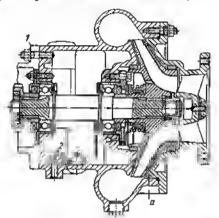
Vista general de una bomba con volutas de dimensiones disminuldas (dibujo de composición)
